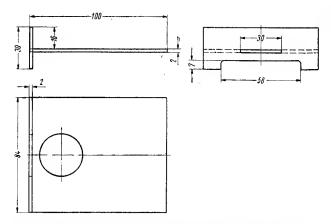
Konstruktive Ausführung der Chassisplatte (Lochdurchmesser und Form der Aussparung sind nach dem verwendeten Lautsprecher festzulegen)
